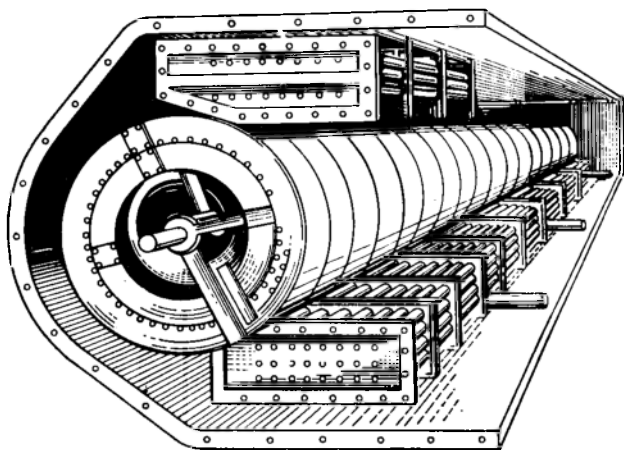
Реактор со шнеком и трубчатыми нагревателями
